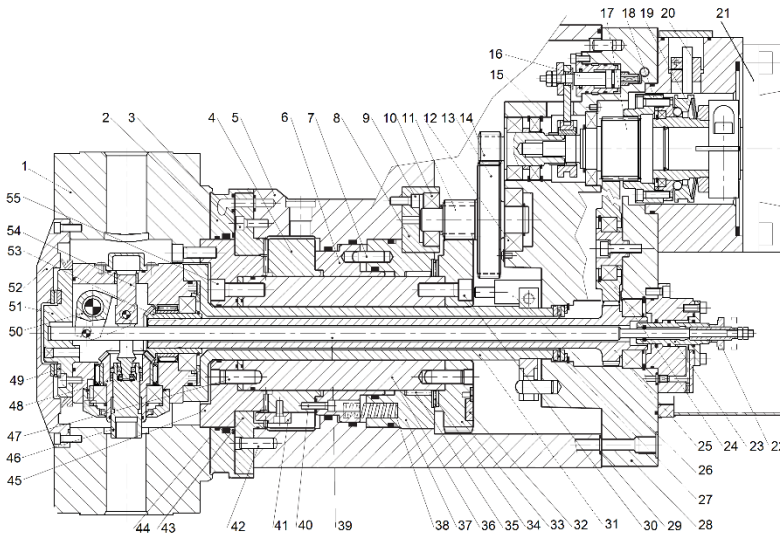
Привід повороту інструментального диску і інструмента револьверної головки SM-BR 16
